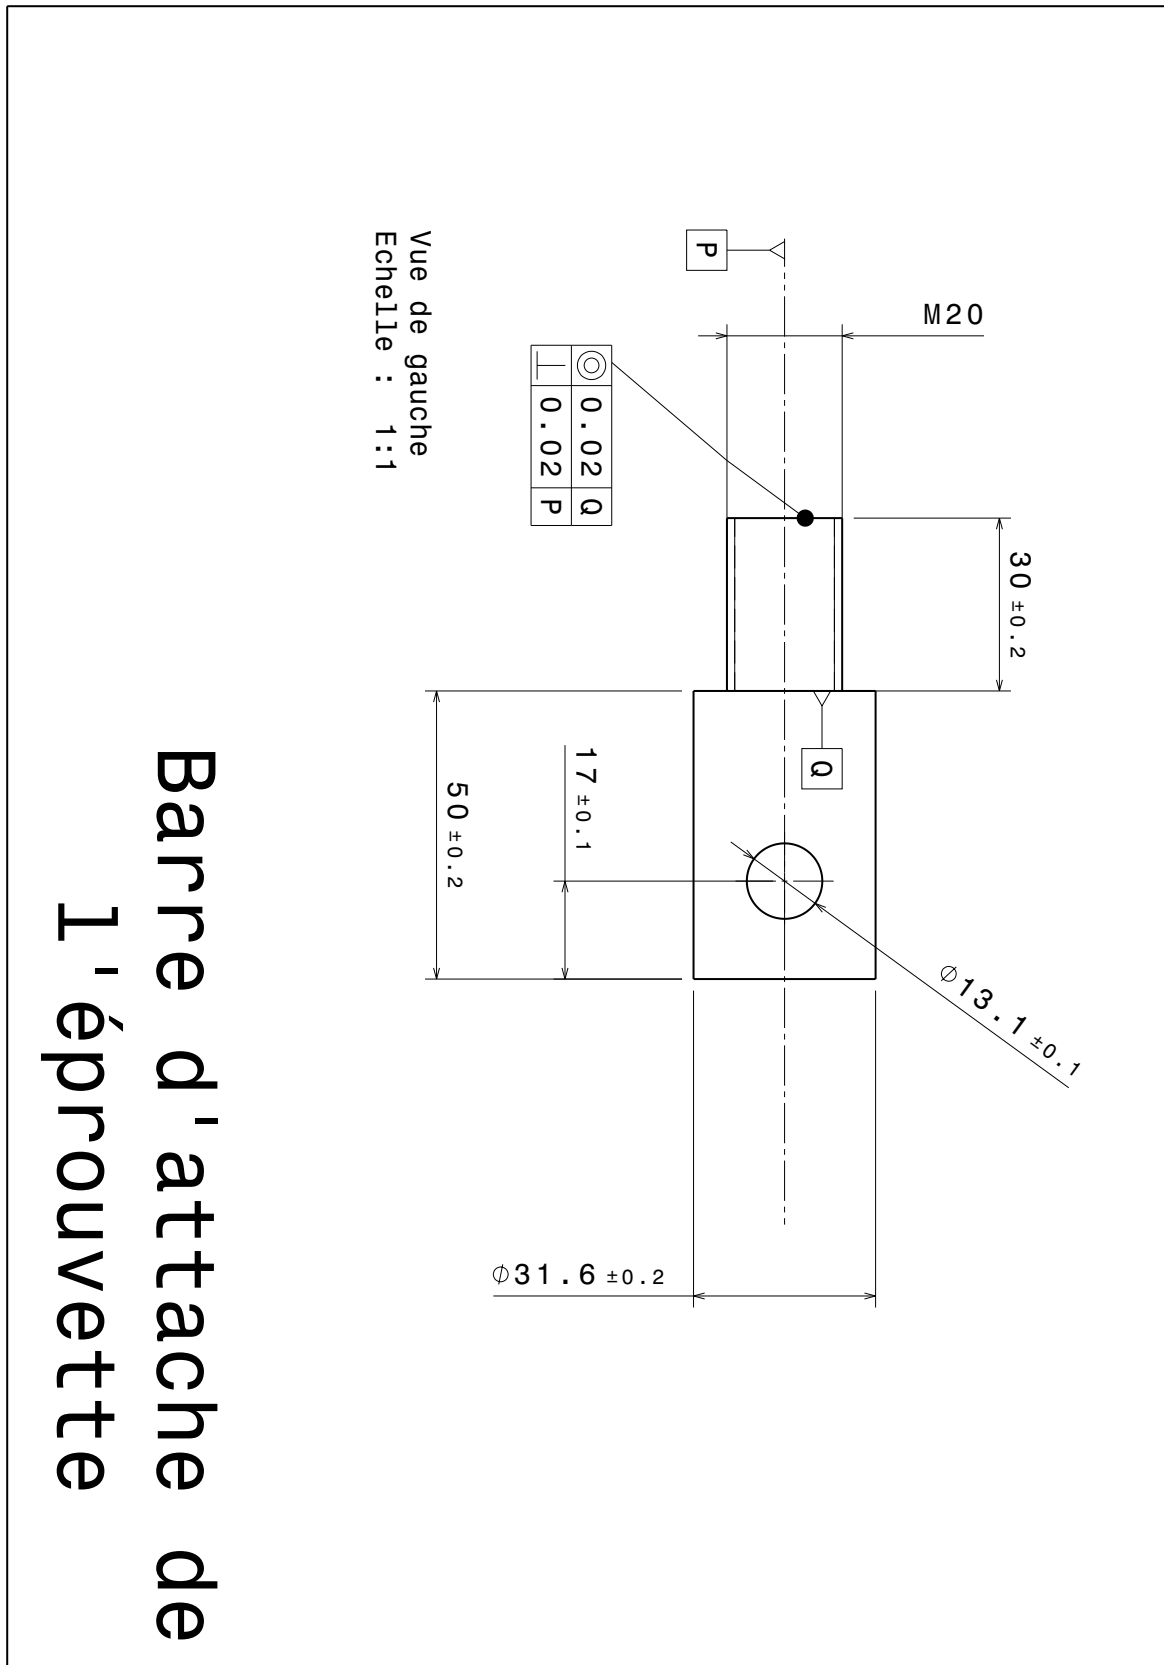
Schéma technique de la barre d'attache de l'éprouvette de peau coffrante
